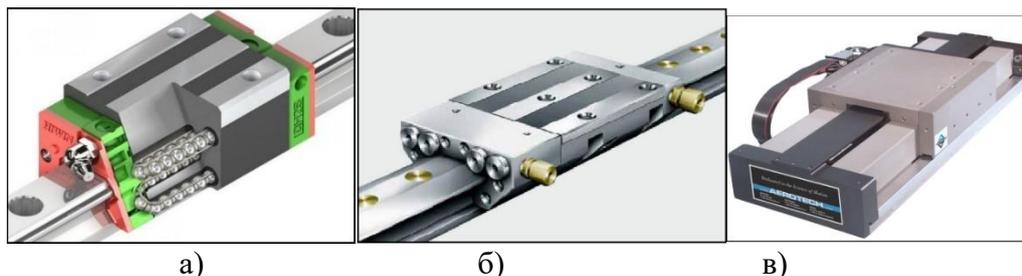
Направляющие, используемые во фрезерных станках с ЧПУ:
